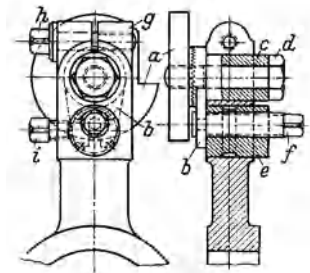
Ausbildung der Planwerkzeuge für Automat nach Abb. 16 zur Aufnahme von Rundformstählen.
